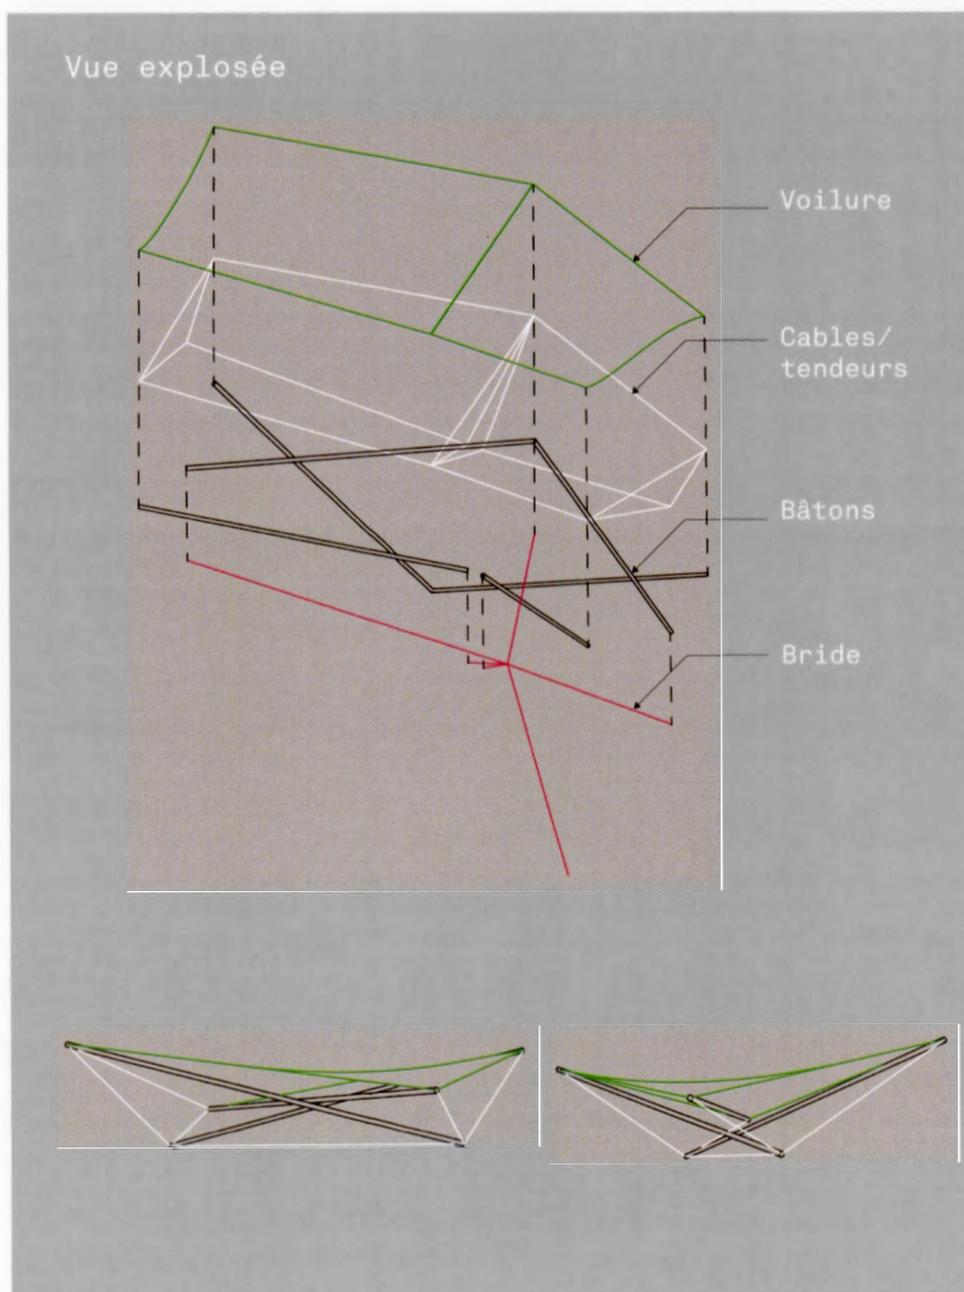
Dessins techniques de planches de présentation : vue explosée, vue 360 degrés de la voilure.
